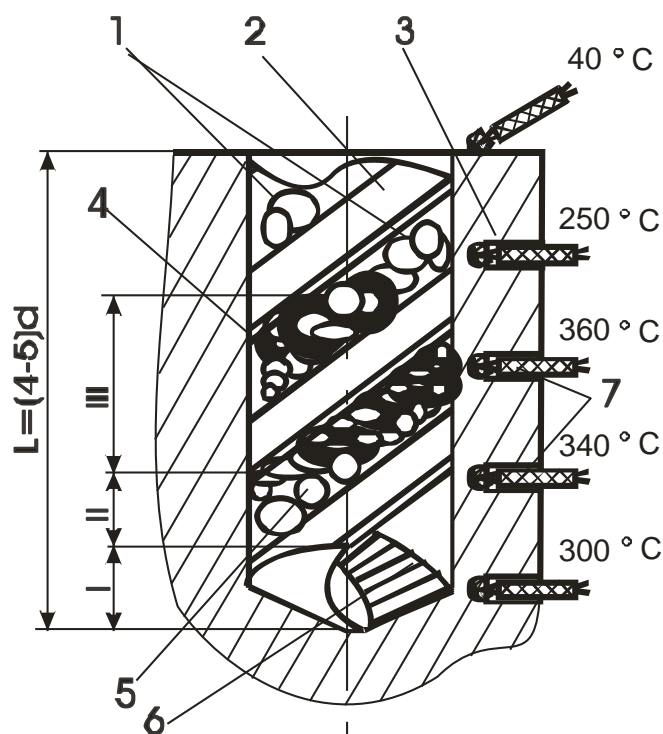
Схема образования пакетов стружки и замера температуры при обработке глубоких отверстий в алюминиевых сплавах по данным работы [4]: 1 - фрагменты элементной стружки и частиц нароста; 2 - спиральное сверло; 3 - обрабатываемая деталь; 4 - плотные пакеты стружки; 5 - сливная стружка; 6 корень стружки; 7 - термопары. I – зона резания и образования сливной стружки с наростами; II – зона образования "рыхлых пакетов" стружки; III – зона образования "плотных пакетов" стружки; IV – зона активного вывода теплоты под действием СОТС
